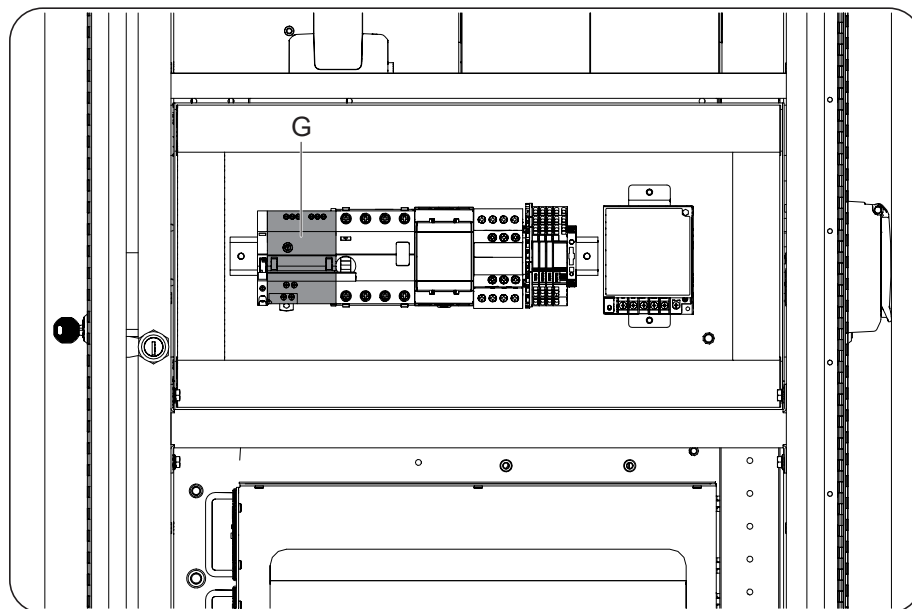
Disposizione dei dispositivi di protezione e controllo carica AC
